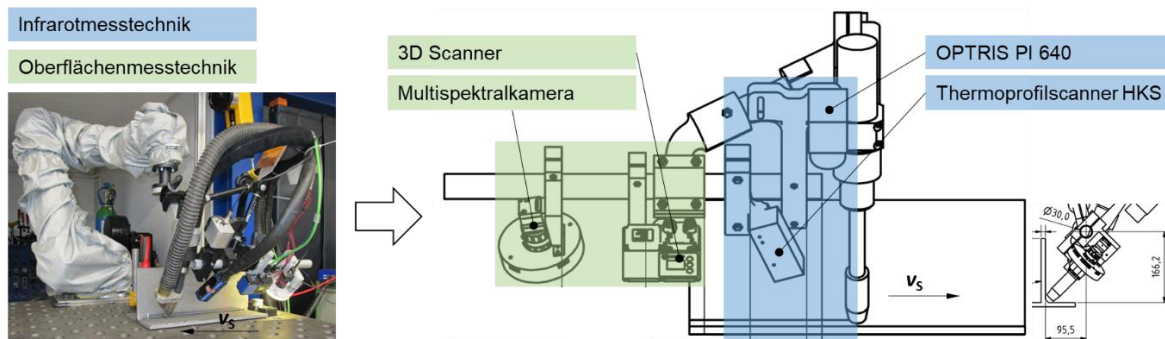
Versuchsaufbau mit Schweißprobe am MRK-10 Roboter
